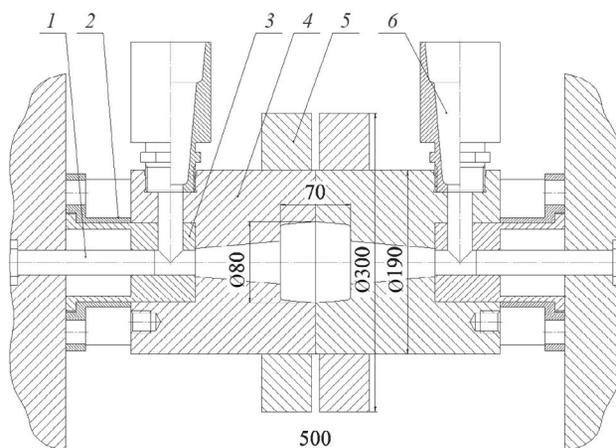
Комплект технологической оснастки для наложения давления: 1 — плунжер прессующий; 2 — основание формы; 3 — камера прессования; 4 — корпус формы; 5 — кольцо (бандаж); 6 — заливочная чаша.
